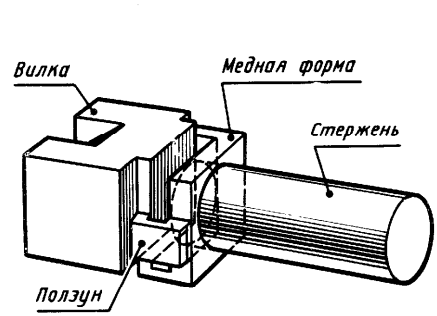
Пример медной охлаждаемой формы для электрошлаковой сварки
